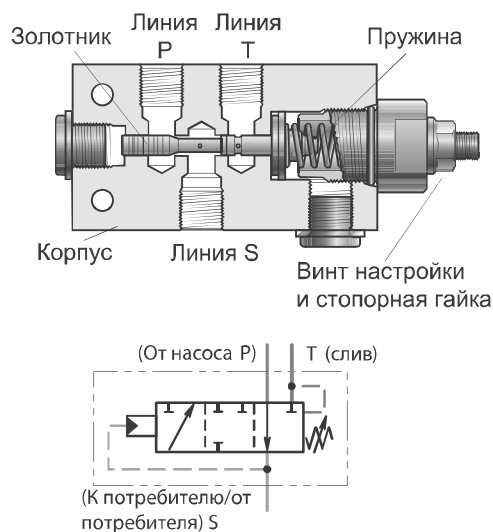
Трёхлинейный редукционный клапан (в разрезе) со схемой
